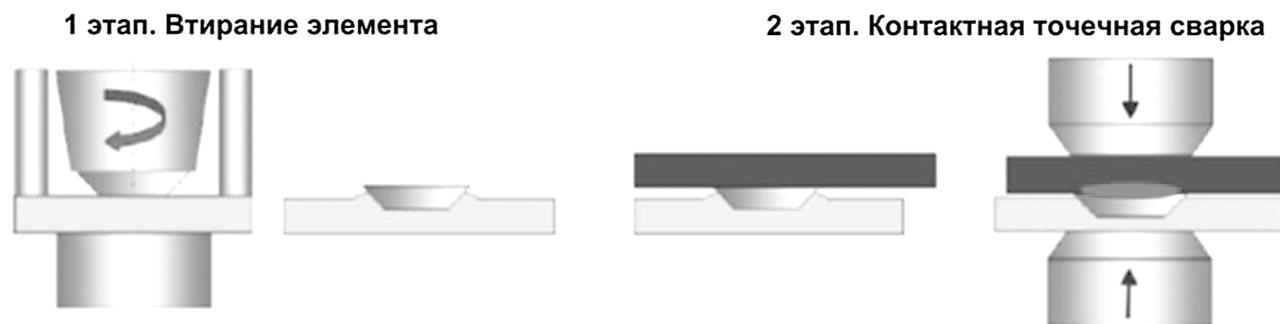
Контактная точечная сварка с внесением вспомогательного элемента при помощи сварки трением [5]
